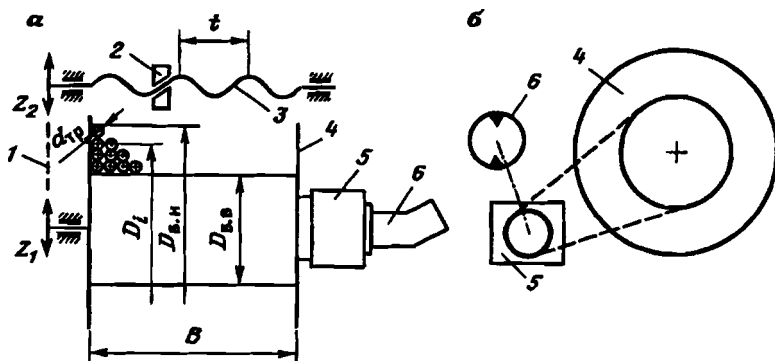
Кинематическая схема барабана для наматывания колонны гибких труб и их укладчика при использовании планетарного редуктора (а) и цепной передачи (б):
